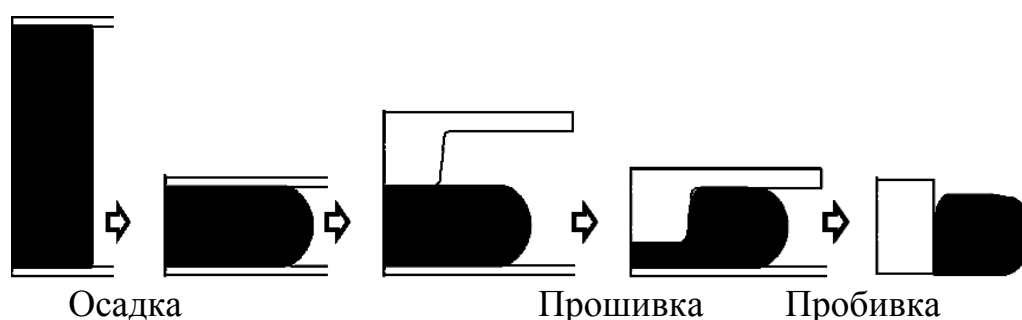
Последовательность ковки кольцевой заготовки из сплава ВТ6
